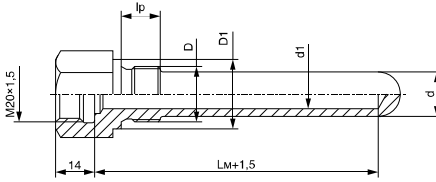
ГТ-702 цилиндрическая для ДТ с подвижным штуцером
